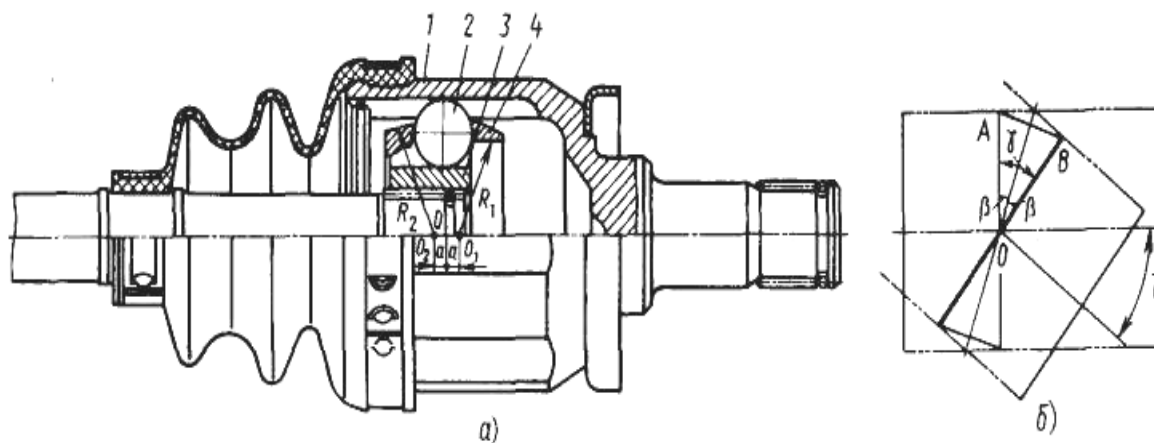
Шестишариковый универсальный карданный (внутренний) шарнир:
